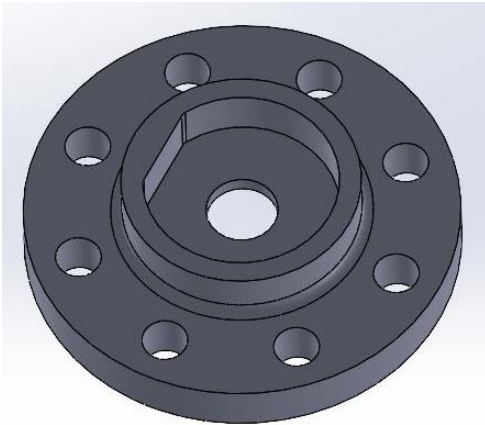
Vista Superior da flange acoplamento ao sensor
